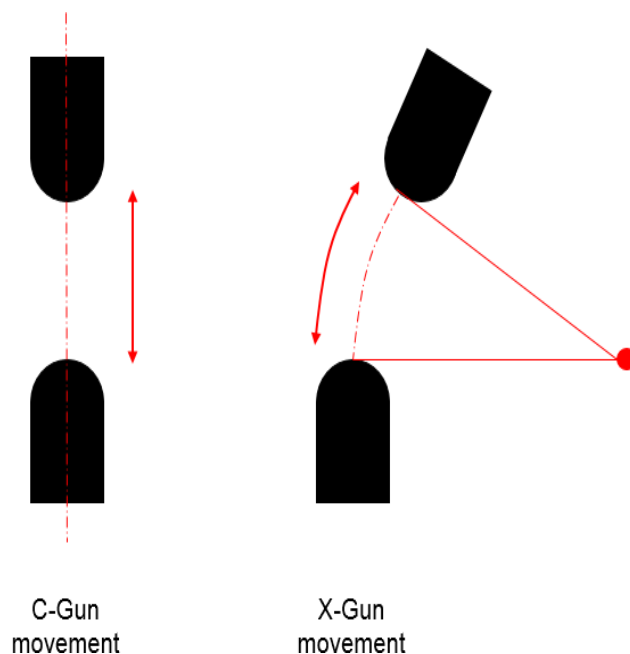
Cinématique du pistolet à spot dans Simufact-Welding.
